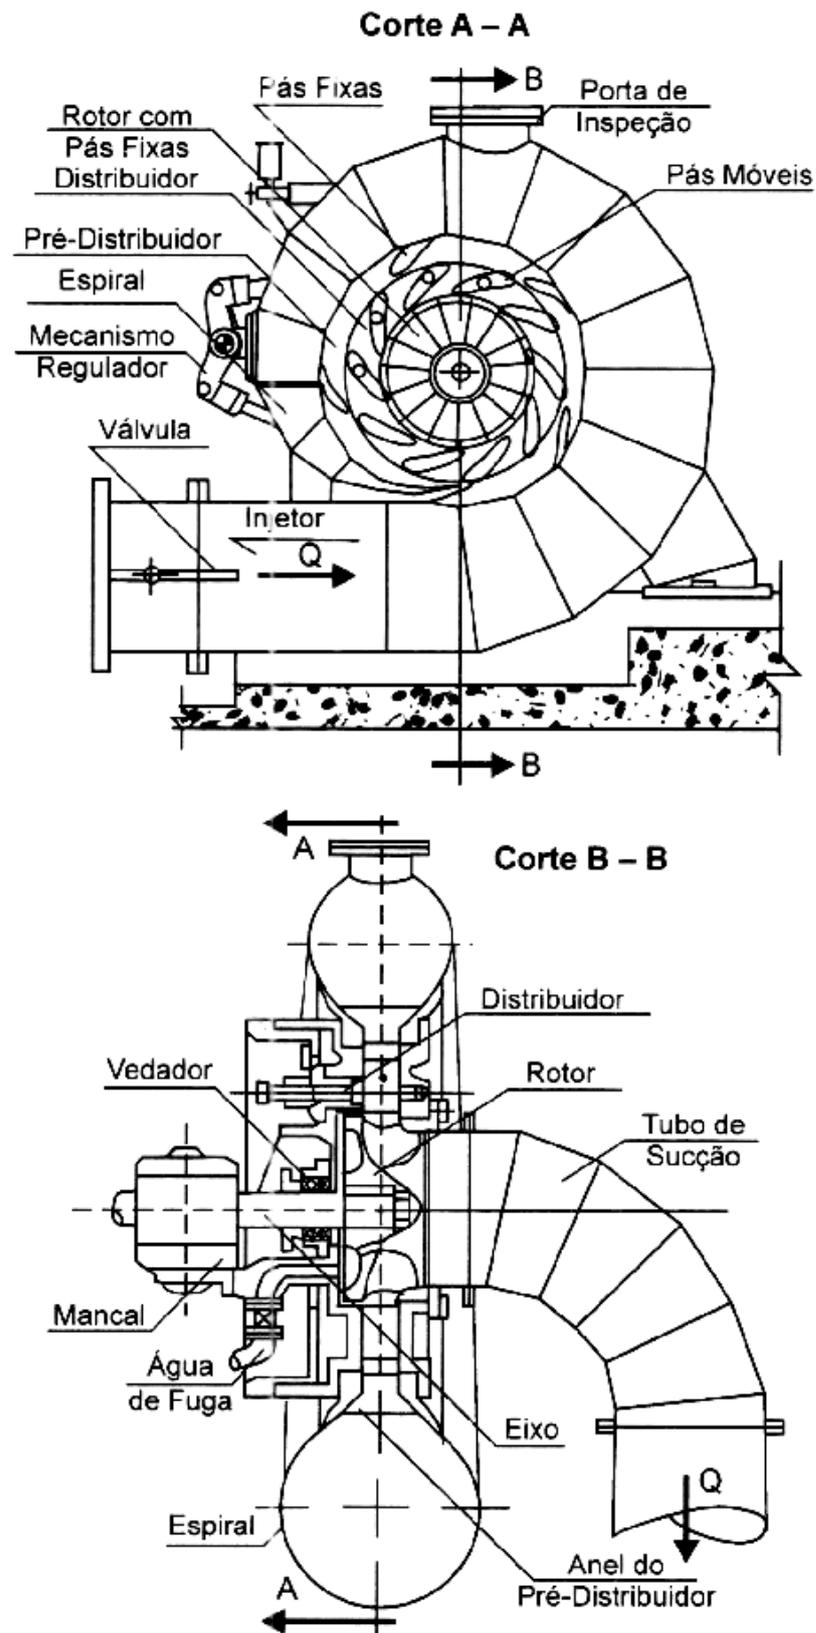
Representação detalhada do conjunto de componentes de uma turbina Francis de eixo horizontal. Fonte: Souza (2009)
